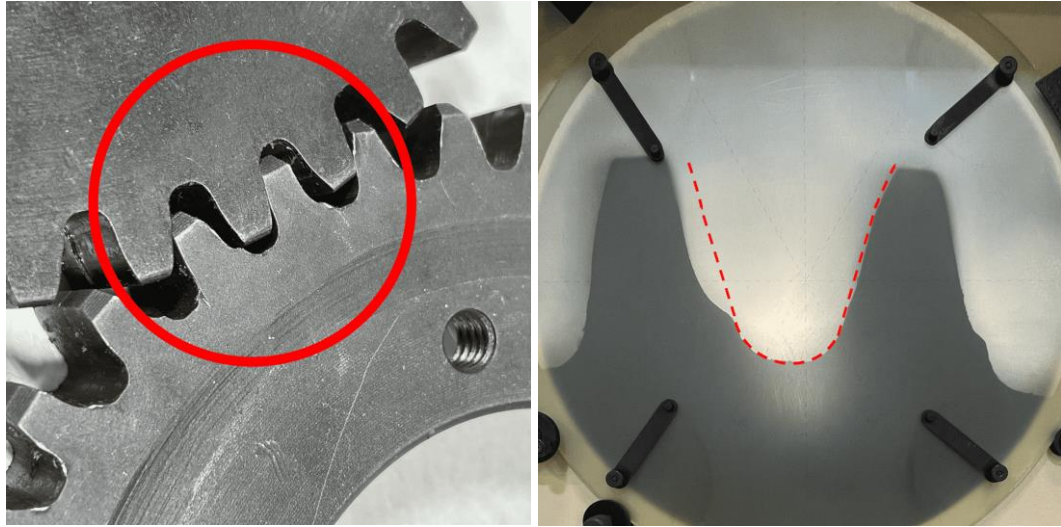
Desgaste excesivo engranaje. Fuente: [24]
